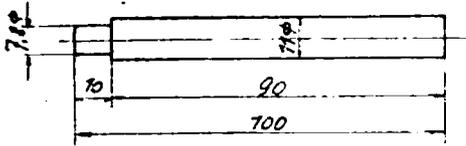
Zum Herausdrücken des Kolbenbolzens ist ein nach dieser Maßskizze anzufertigender Dorn zu verwenden
